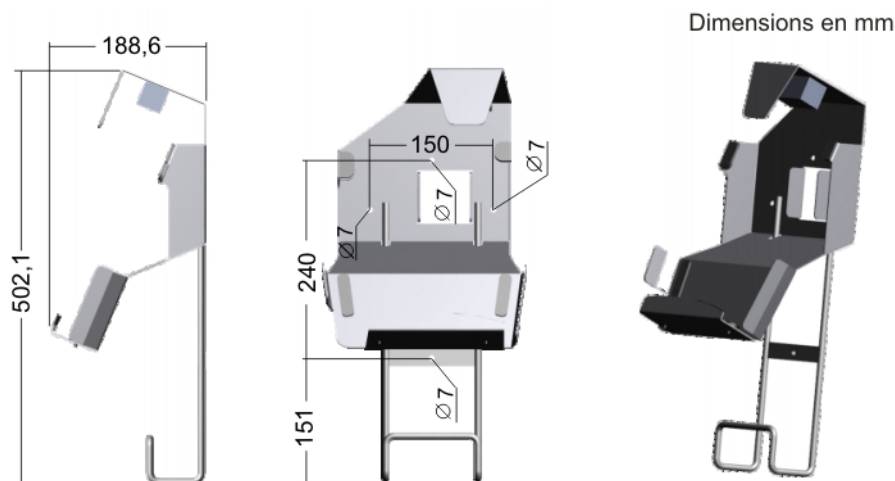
Dimensions et cotes de perçage du support smartPAD
